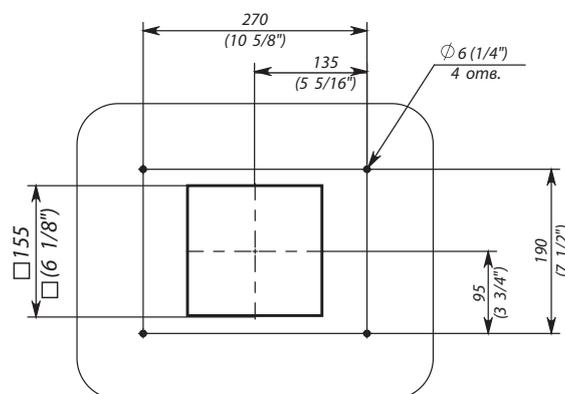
Схема разметки отверстий под крепеж наружных боксов
